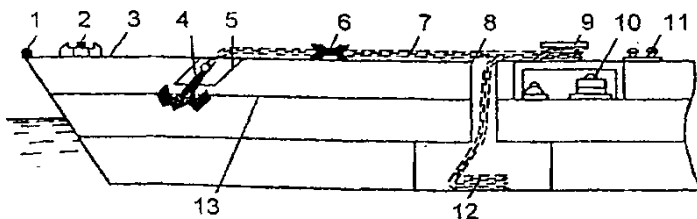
Якорное устройство: 1 – носовой полуклюз; 2 – киповая планка; 3 – верхняя палуба; 4 – якорь; 5 – якорный клюз; 6 – стопор якорной цепи; 7 – якорная цепь; 8 – палубный клюз; 9 – якорно-швартовный шпиль; 10 – отделение якорно-шпильевых двигателей; 11 – кнехт; 12 – цепной ящик; 13 – нижняя палуба
